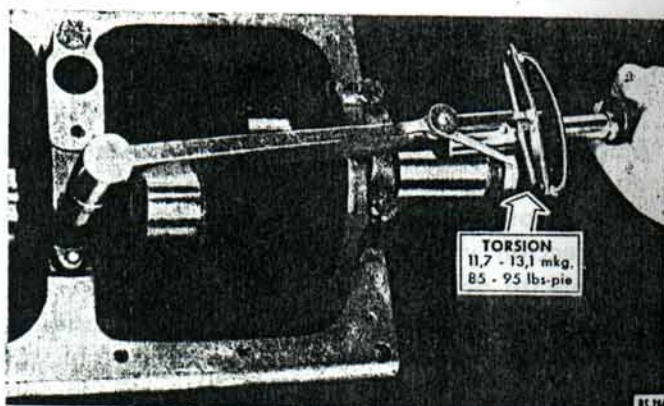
Ajustando las tapas de los cojinetes de bancada.
